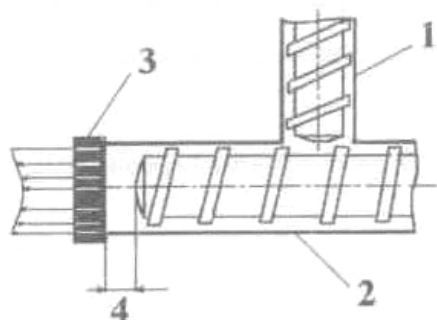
Схема прессования пороховых масс шнек-прессом Ш-2В [8]:
